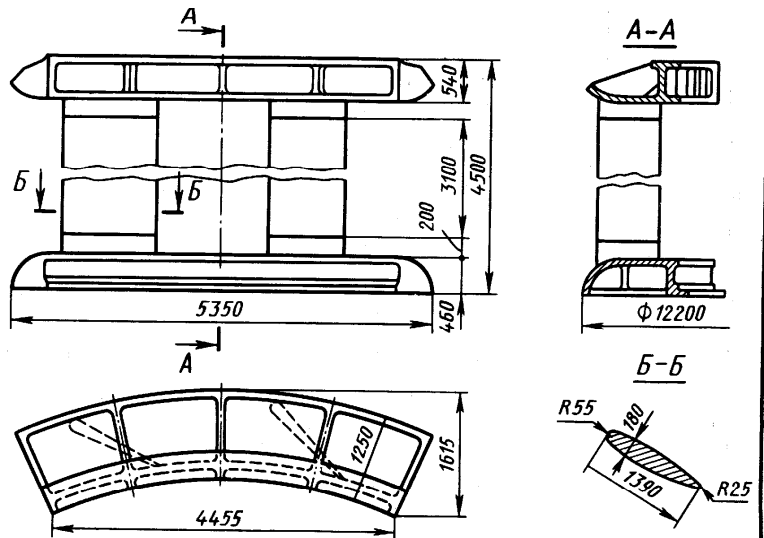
Сварно-литой статор гидротурбины, выполненный электрошлаковой сваркой
